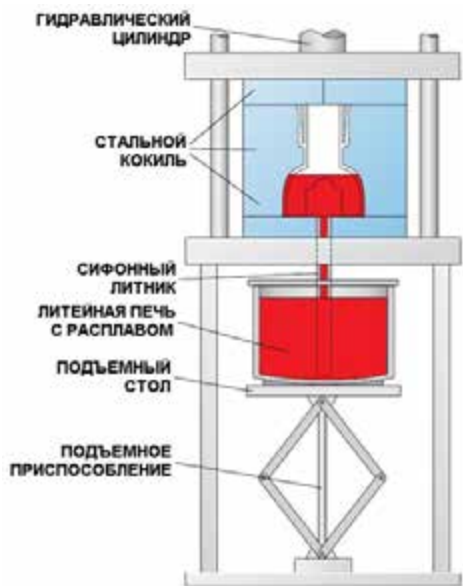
ro-10: Схема литья в кокиль под низким давлением; источник: MSI
